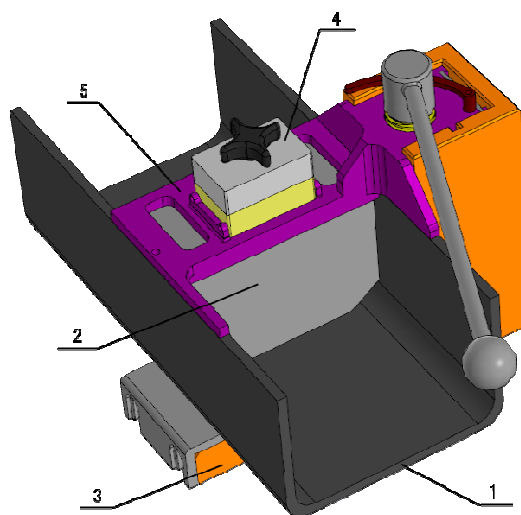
3D модель узла приспособления для сборки направляющей двери крытого грузового вагона:
